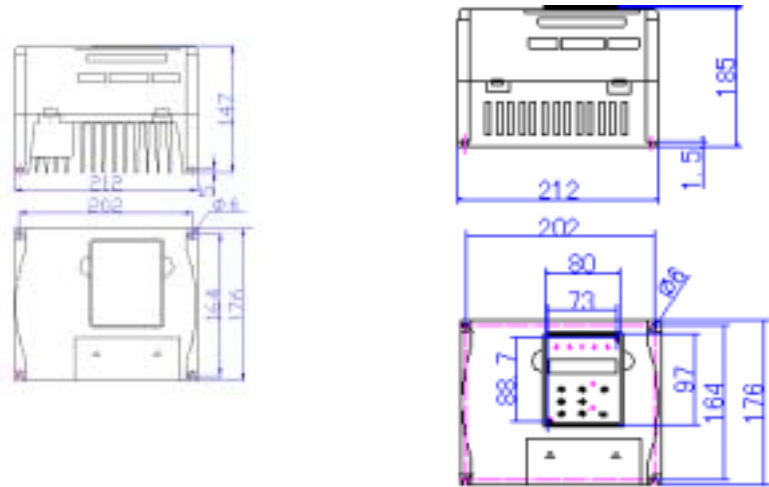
为 2.2kw ~ 5.5kw 外形尺寸及安装尺寸 图 3 为 7.5kw ~15kw 外形尺寸及安装尺寸
